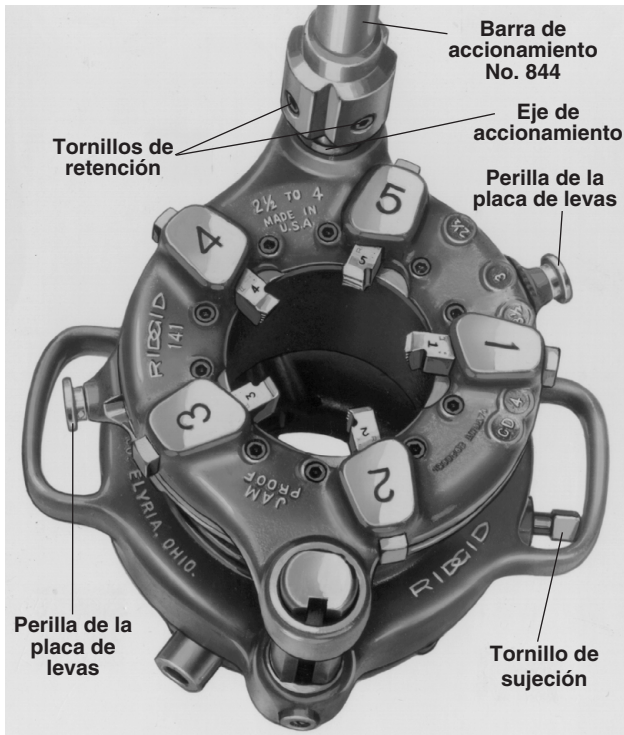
Roscadora a Engranajes No. 141 con la barra de accionamiento No. 844 instalada
